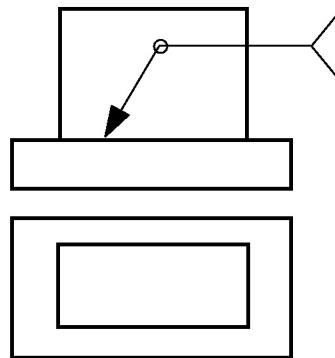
Soldadura «todo alrededor» del perímetro visible en la planta
